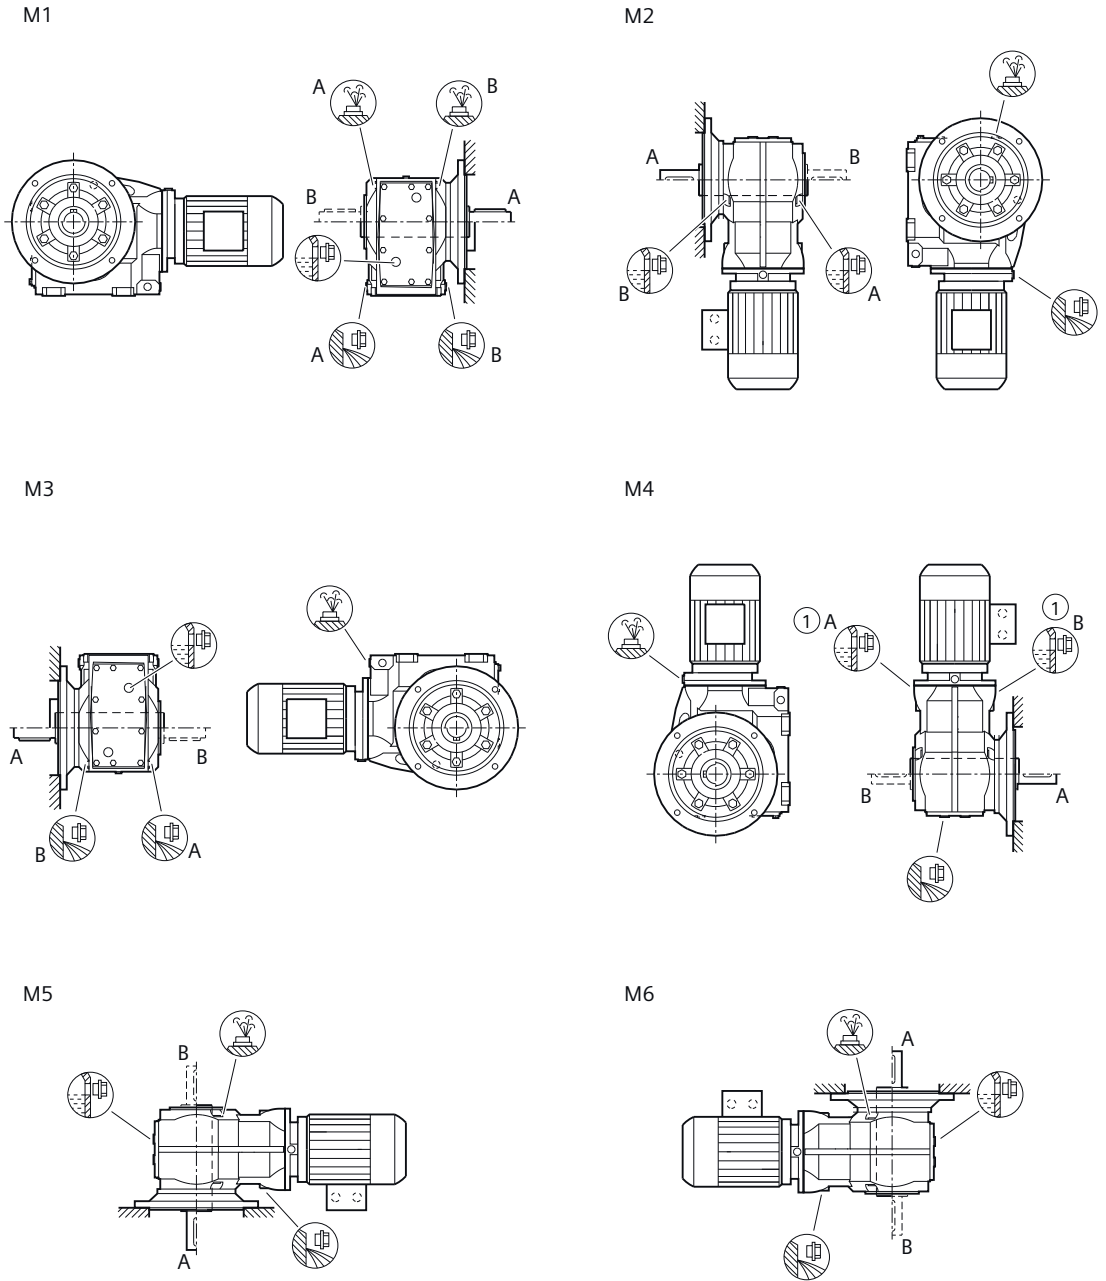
Konik dişli için montaj konumları BAD Geçmeli model Boyutlar 39 - 49
